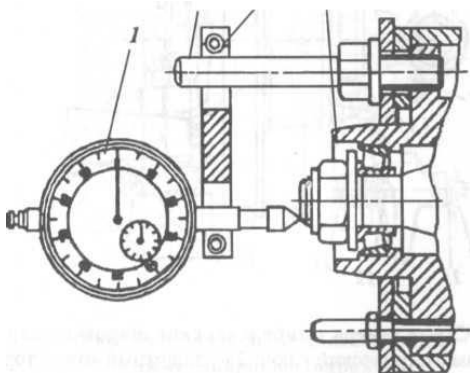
Схема проверки осевого зазора в подшипниках ступиц передних колес:
